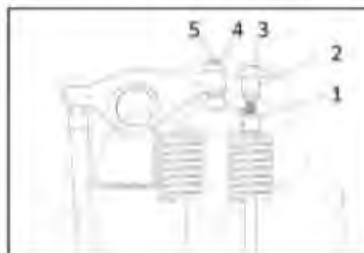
Регулировка зазора выпускных клапанов для двигателя с WEVB
